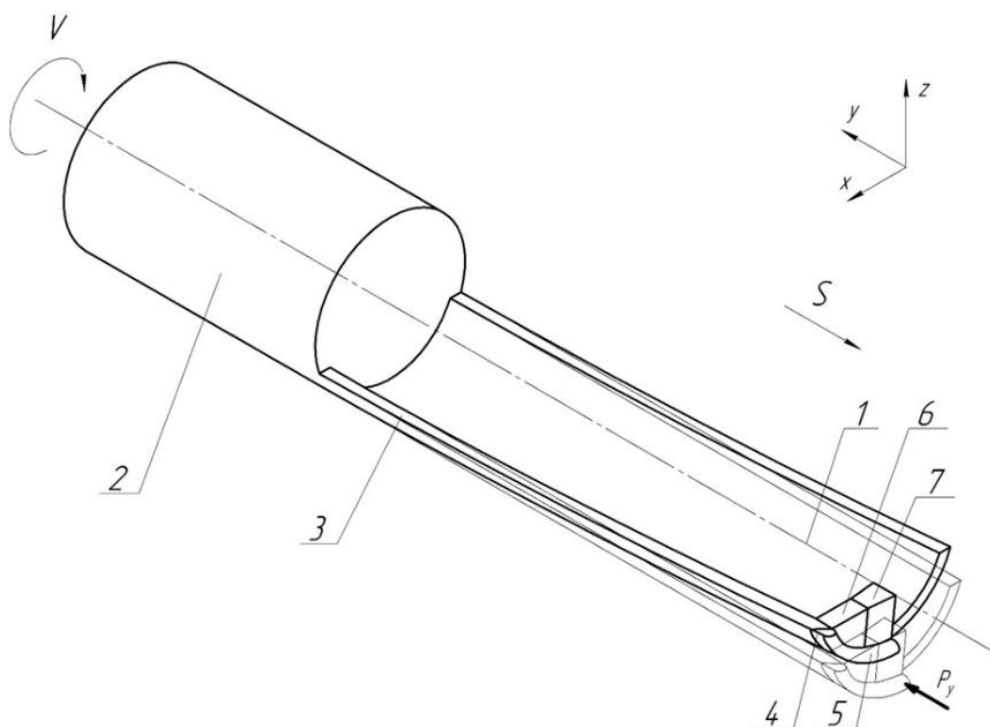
Режущий инструмент, предназначенный для выемки стержня из несквозного отверстия, полученного кольцевым сверлением
